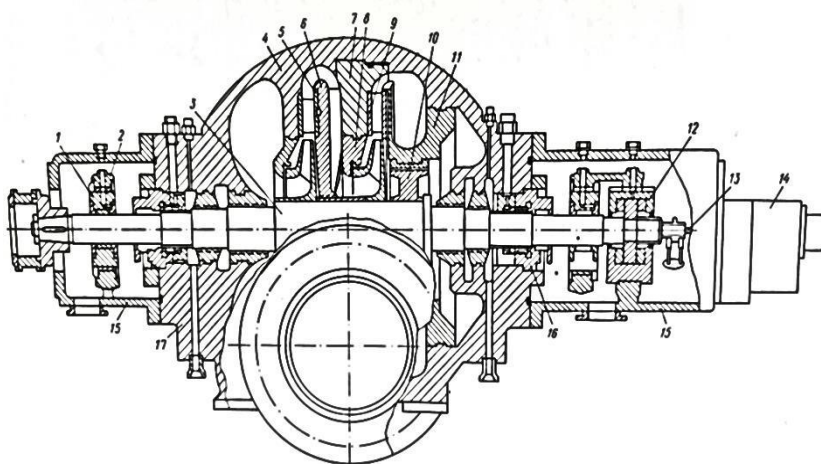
Газоперекачувальний агрегат ГПА-Ц-6,3/56
